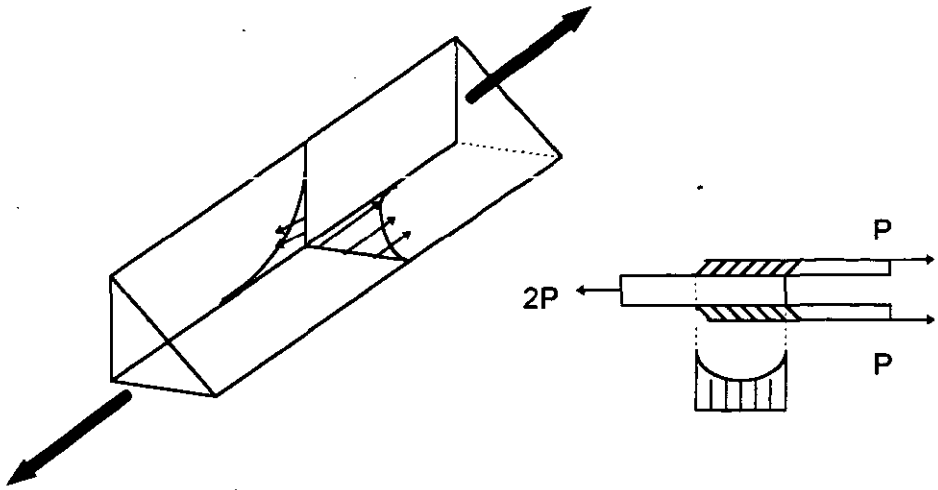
Esfuerzos en soldaduras de filete cargadas longitudinalmente.
